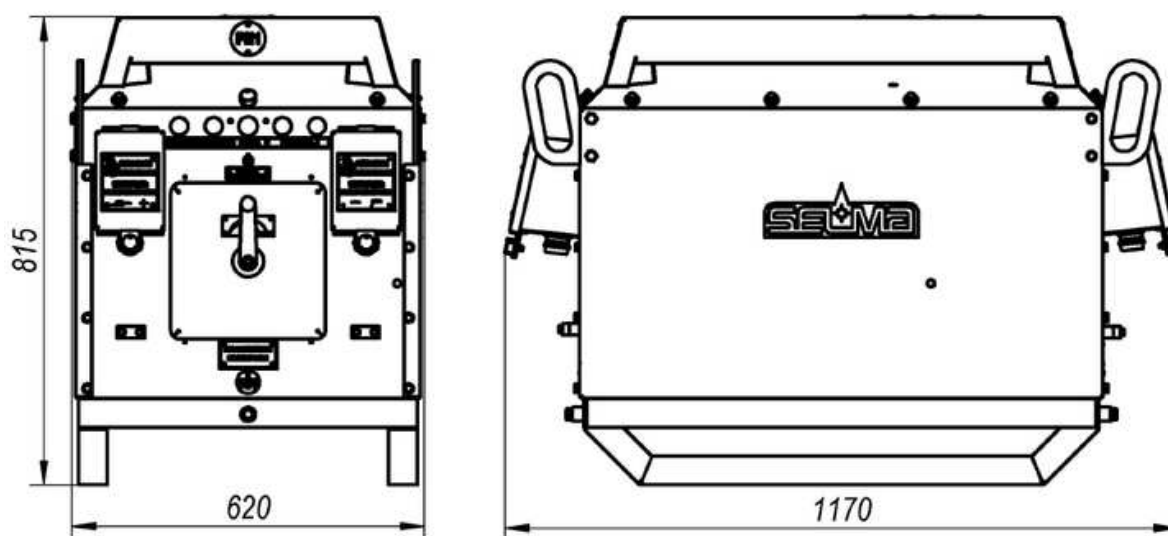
Общий вид и габаритные размеры сварочного выпрямителя Горняк 500
